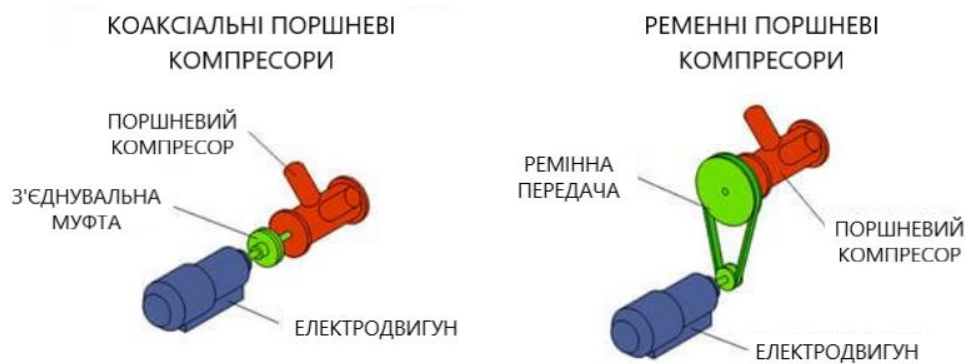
Типова конструкція коаксіального та ремінного компресорів
